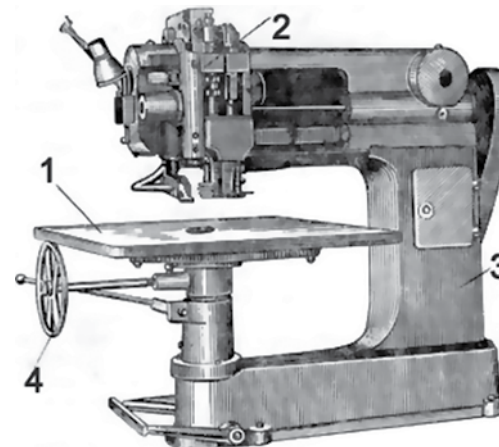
Станок для высверливания и заделки сучков СвСА: 1 – рабочий стол; 2 – суппорт с двумя рабочими шпинделями; 3 – станина; 4 – маховичок для установки стола по высоте
